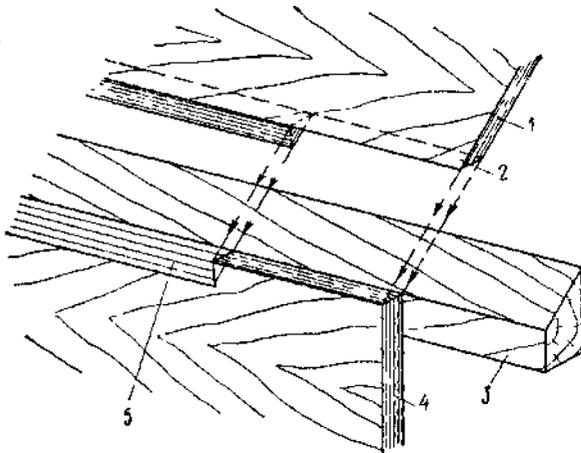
Подгонка листов обшивки на скуловом стрингере (сборка корпуса — вверх килем).
